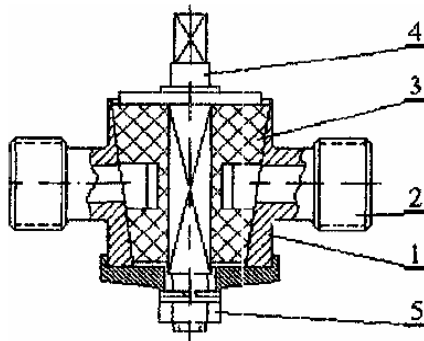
Схема розподільчого крана: 1 – корпус; 2 – ніпель (4 шт.); 3 – шибер; 4 – валик; 5 – дозволяючі шайба з гайкою
